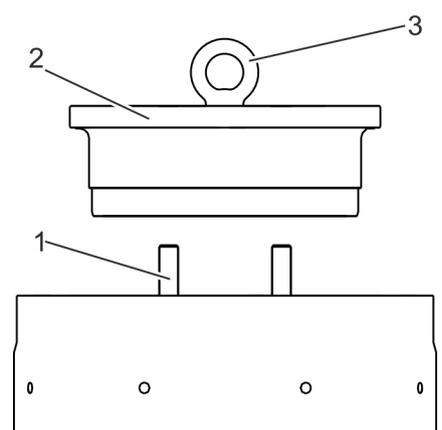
Vissage des anneaux de levage dans le couvercle de serrage
